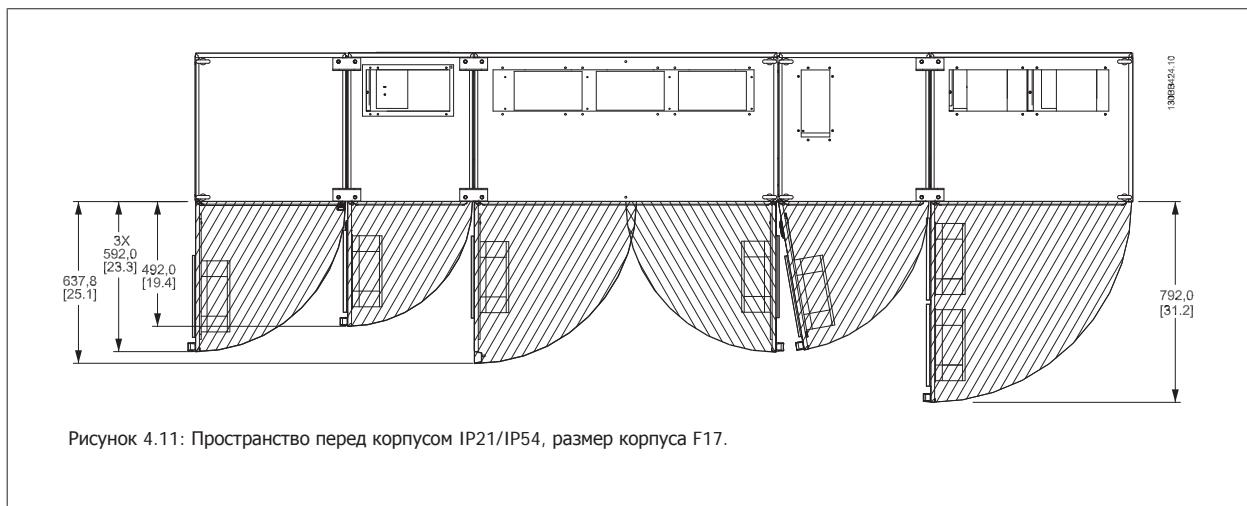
Пространство перед корпусом IP21/IP54, размер корпуса F17.
